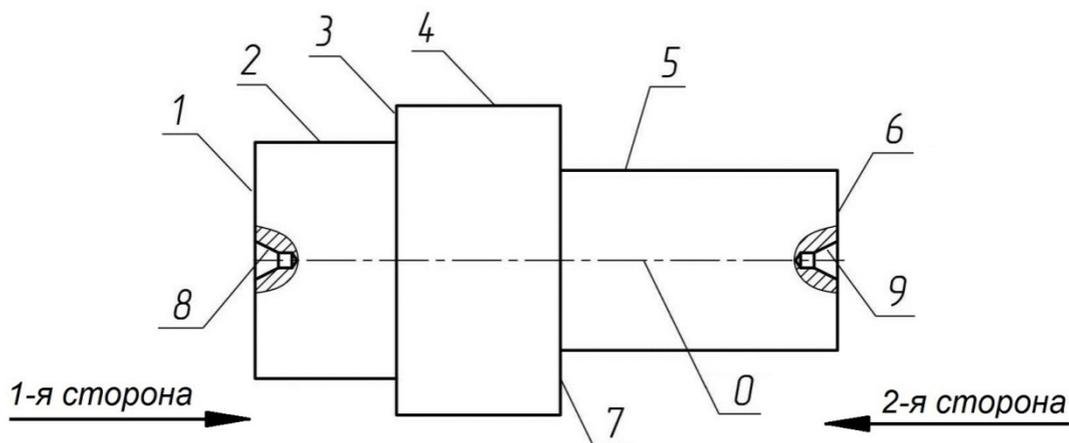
Пример выявления и обозначения элементарных поверхностей
